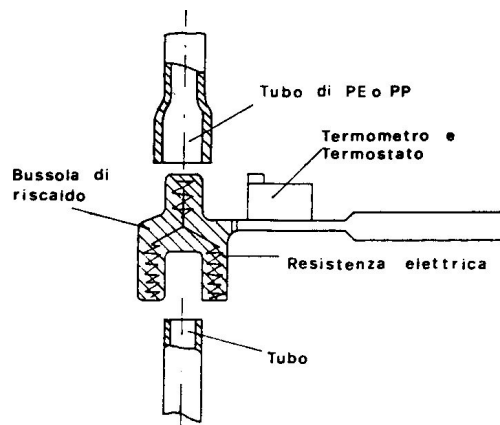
Giunto per tubi di PEAD per polifusione nel bicchiere.
